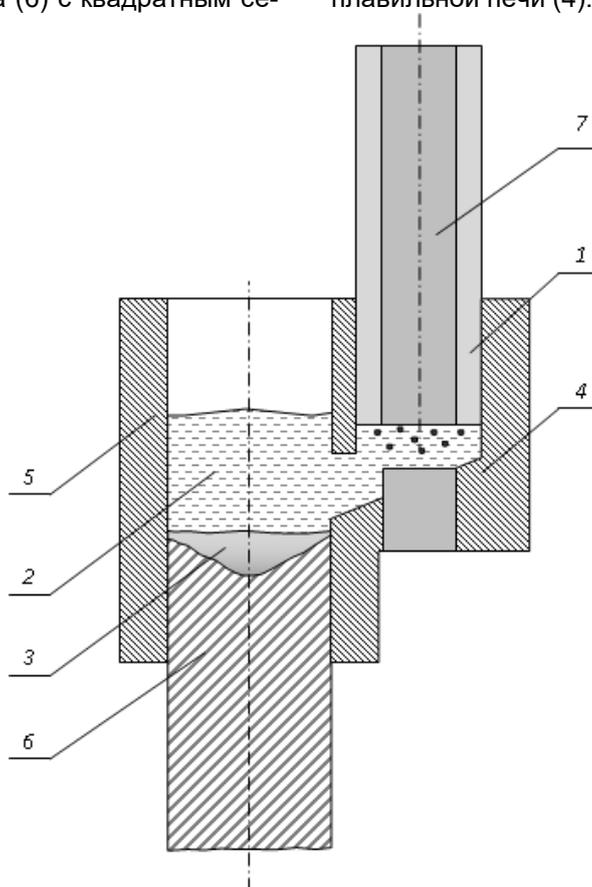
Схема установки: 1 – мундштук; 2 – жидкий шлак; 3 – жидкий металл; 4 – плавильная печь; 5 – литейная форма; 6 – отливка; 7 – расходуемый электрод
